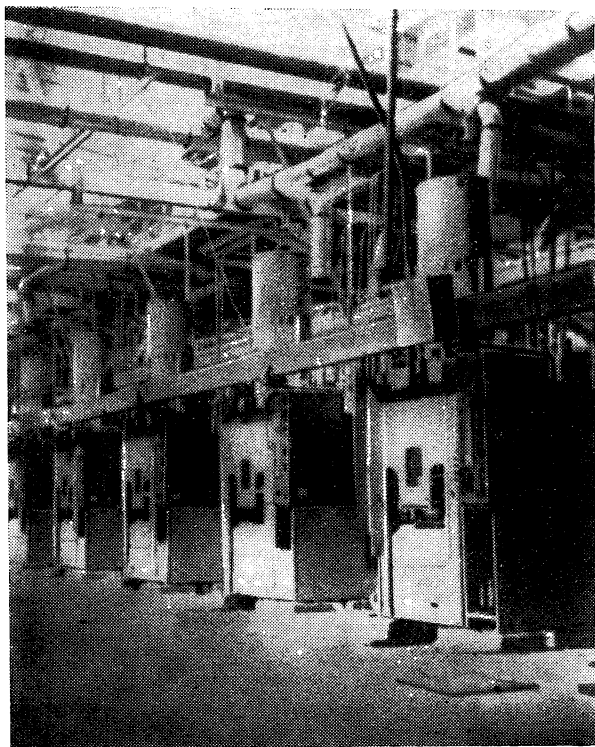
Общий вид участка цеха изготовления формовых изделий в литевых прессах.
